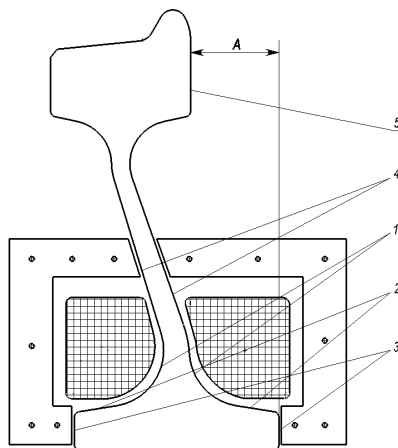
Схема профиля индукционного нагревателя и колеса
